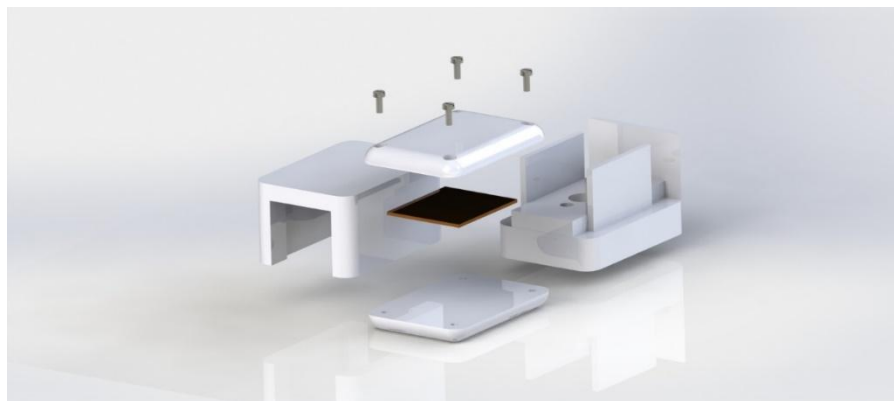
Вигляд розбору повного корпусу
